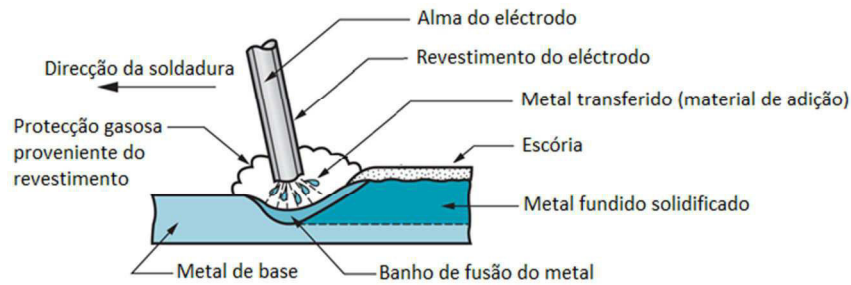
Soldadura por eléctodos revestidos (SMAW) [FONTE: adaptado [58]].
